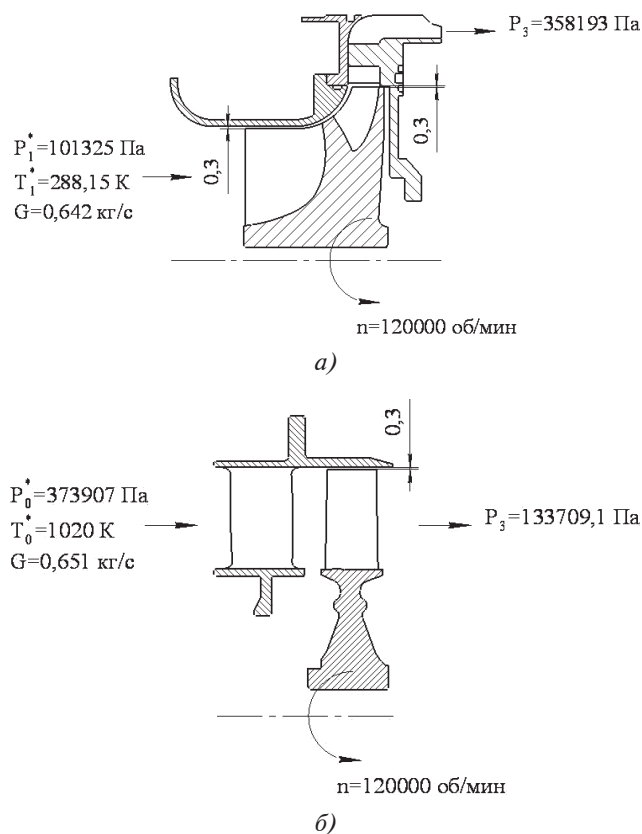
Конструктивные схемы: а — компрессора; б — турбины
